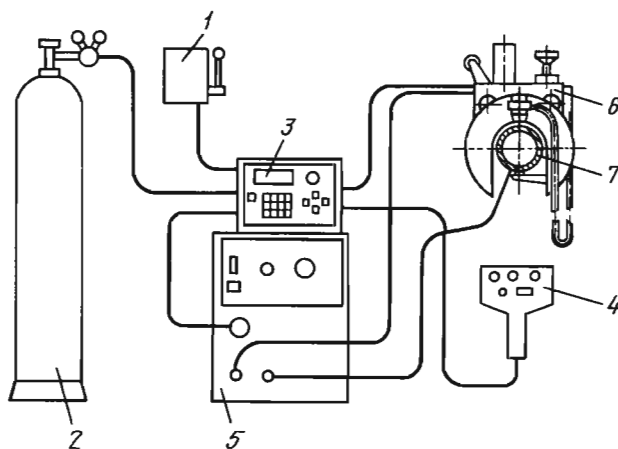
Типовая схема поста автоматической сварки в защитном газе:
